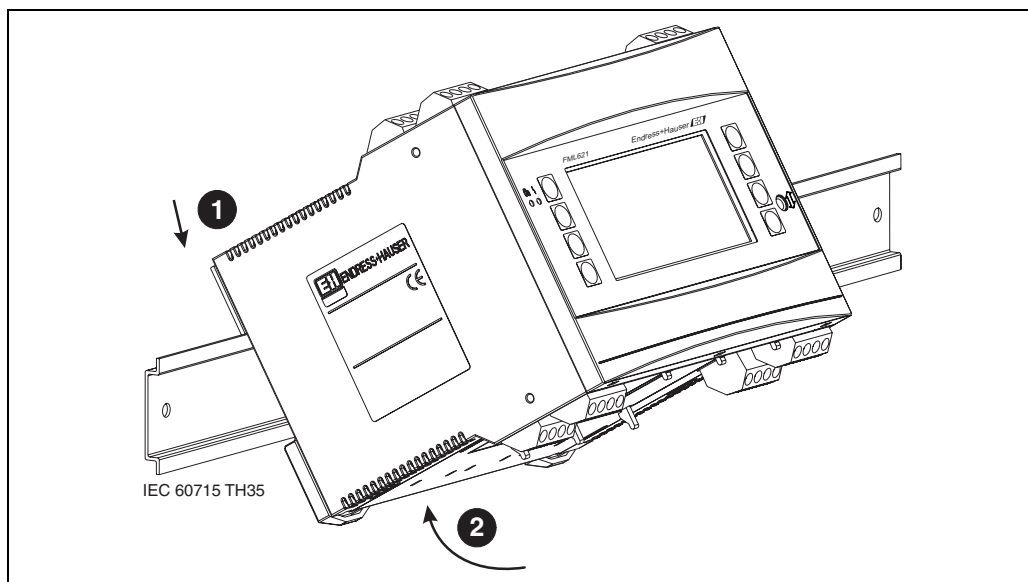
Montaje del equipo sobre el carril de fijación superior
